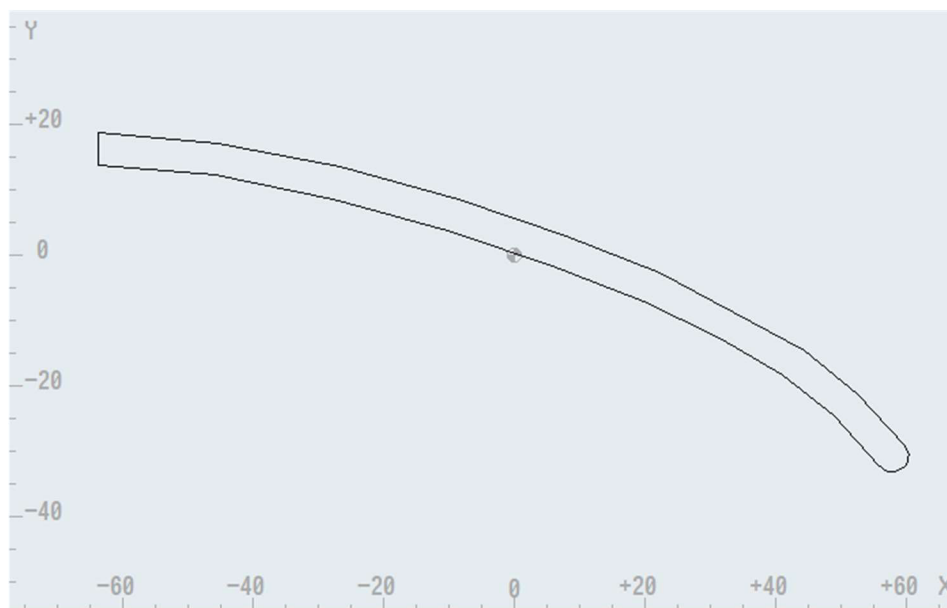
Nezdařilý import dxf souboru pomocí CAD Readeru.
